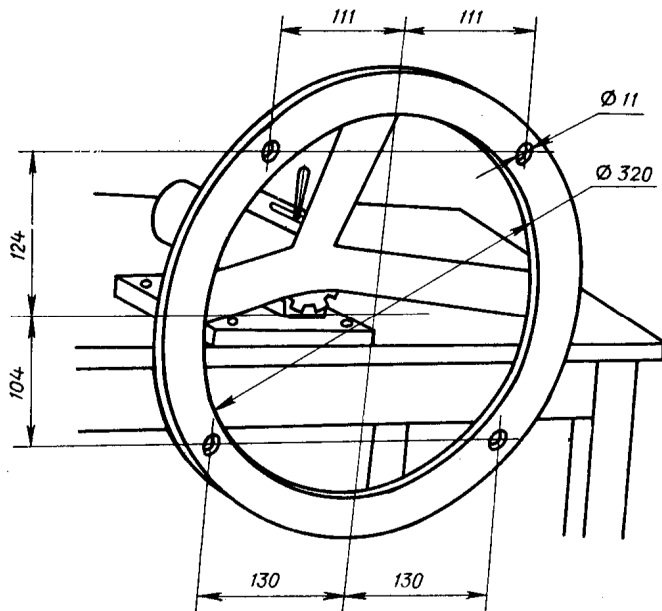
Приспособление для крепления двигателя при разборке и сборке
